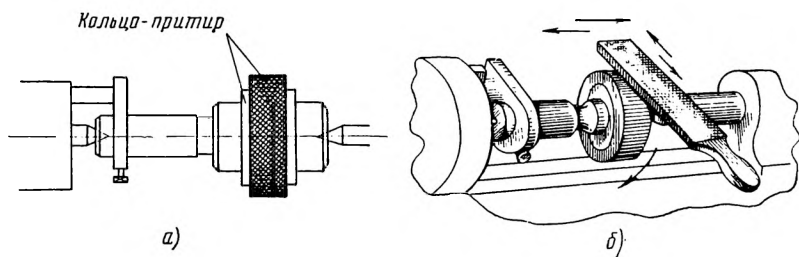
Схемы установки калибра-пробки на токарном станке:
